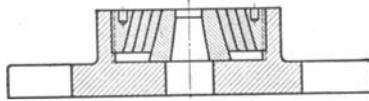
Auswechselbare Schnittplattenbefestigung.
